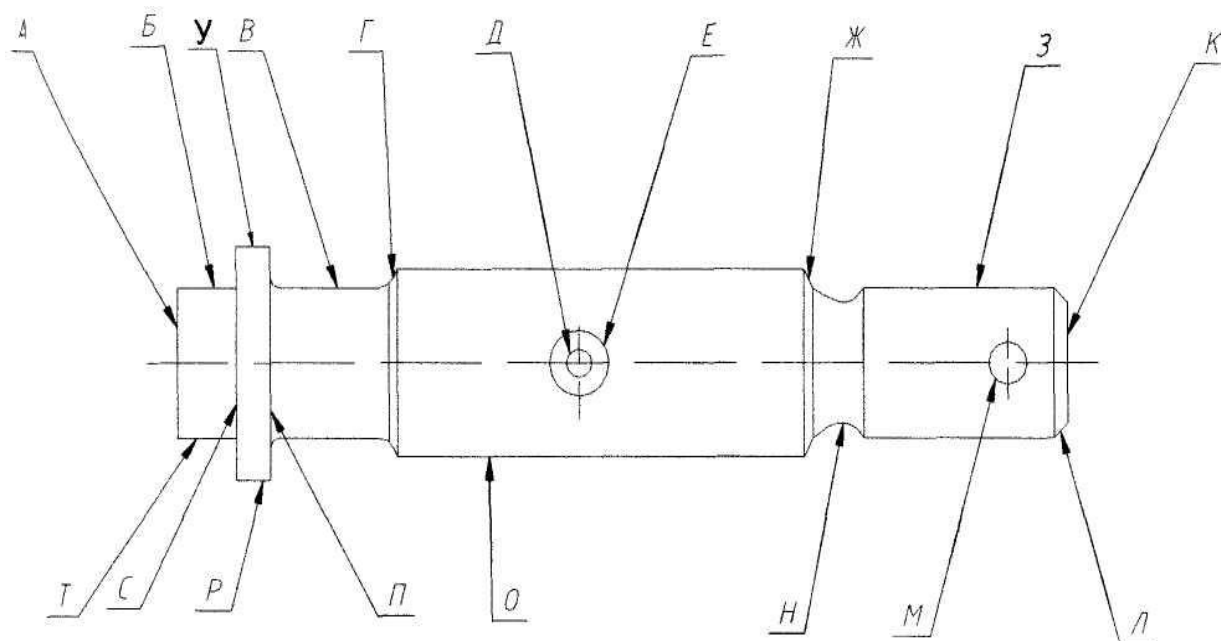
Схема деталі з позначеними поверхнями
